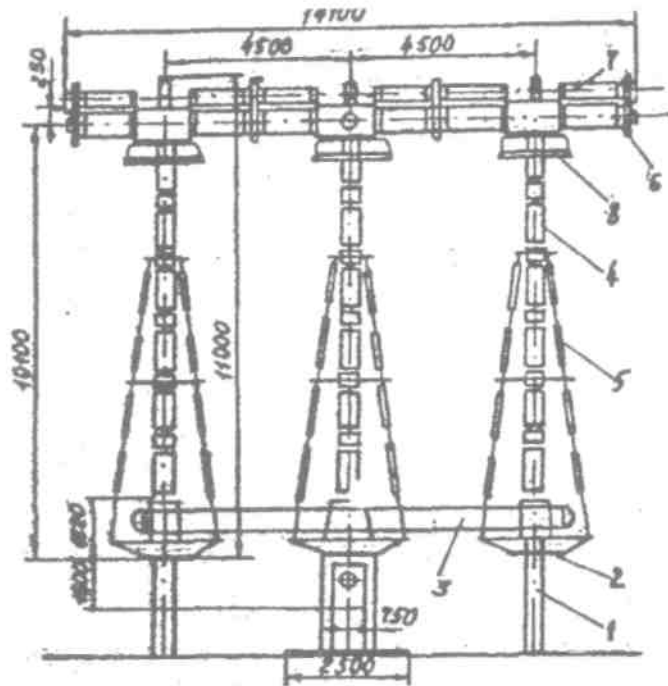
полюс воздушного выключателя ВНВ-750: 1 — опорная конструкция; 2 — рама; 3 — резервуар; 4 — изоляторы опорной колонки; 5 — растяжка; 6 — дугогасительная камера; 7 — конденсатор; 8 — экранное кольцо
